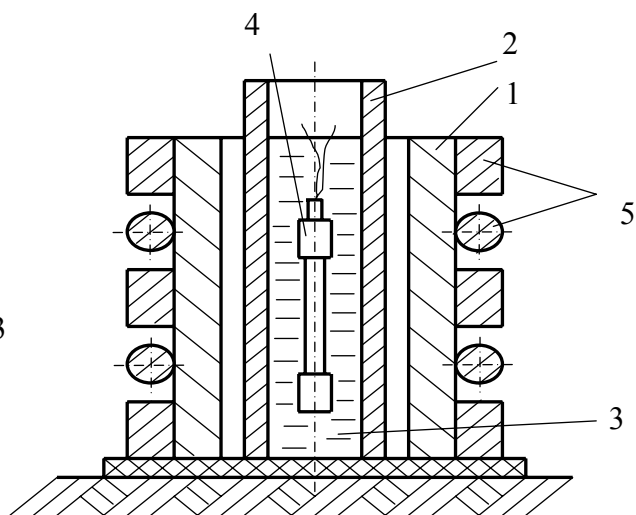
Схема процесса штамповки взрывом гильз кристаллизаторов:
